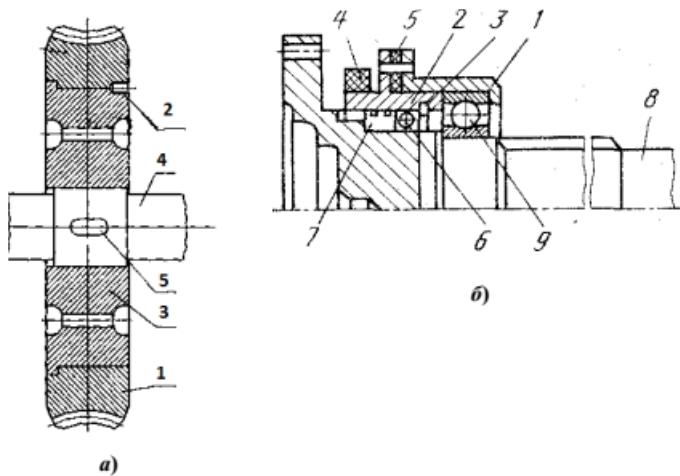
Фрагменты чертежей сборочных единиц:
